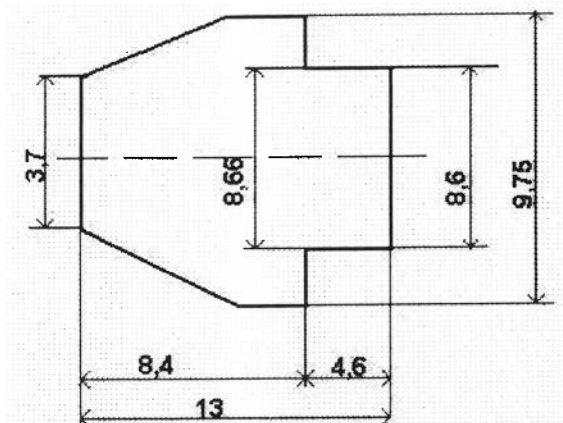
Desenho dimensional do tampão utilizado na fabricação das varetas combustível e nos corpos de provas.
